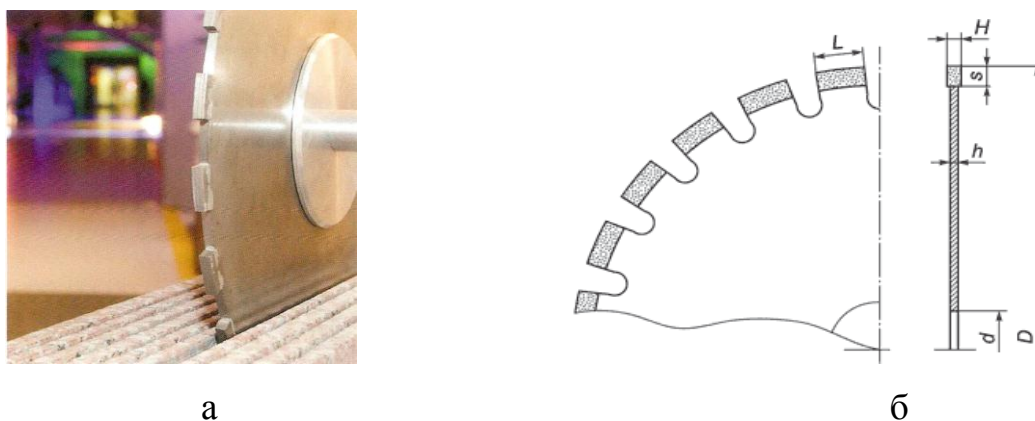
Общий вид дискового алмазного инструмента: а- процесс распиловки природного камня на станке; б- конструктивная схема дисковой алмазной пилы.
